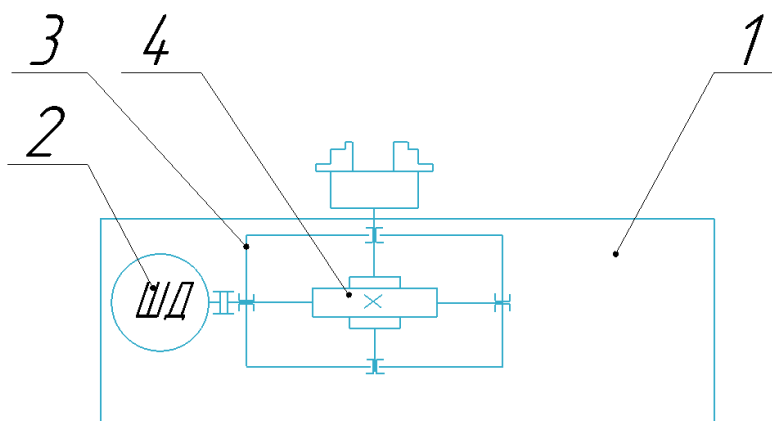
Кинематическая схема (1 – стол; 2 – привод шпинделя; 3 – корпус; 4 - червячная передача; не указаны подшипники качения и скольжения)
